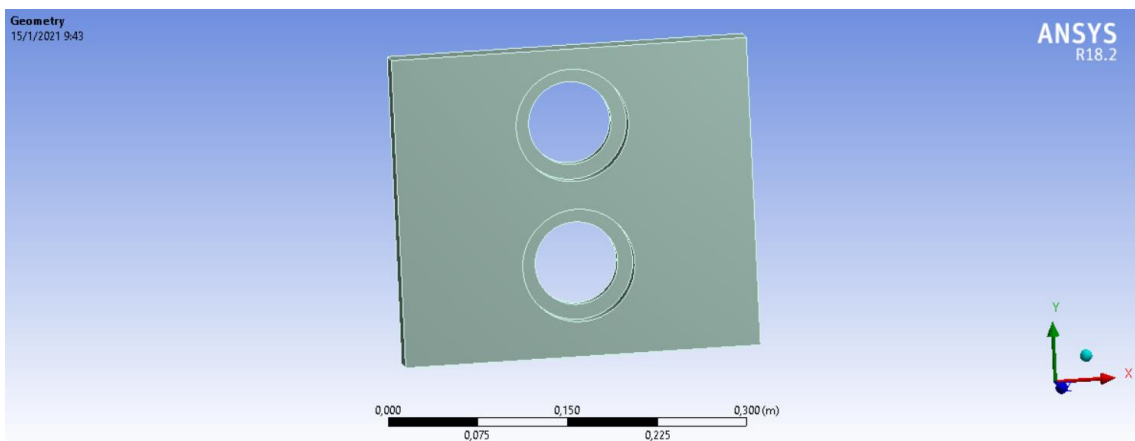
Definición de geometría - bastidor izquierdo de laminado
